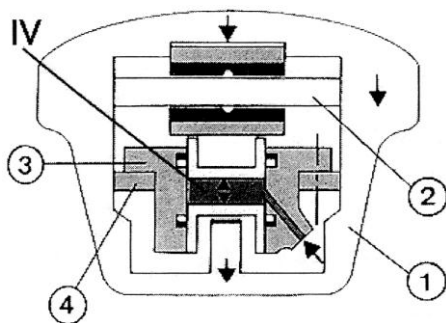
Схема дискового тормозного механизма с подвижной направляющей колодок:
